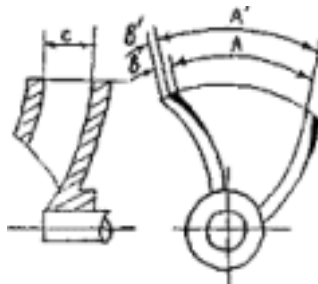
Схема підрізування робочого колеса по лопатках.
